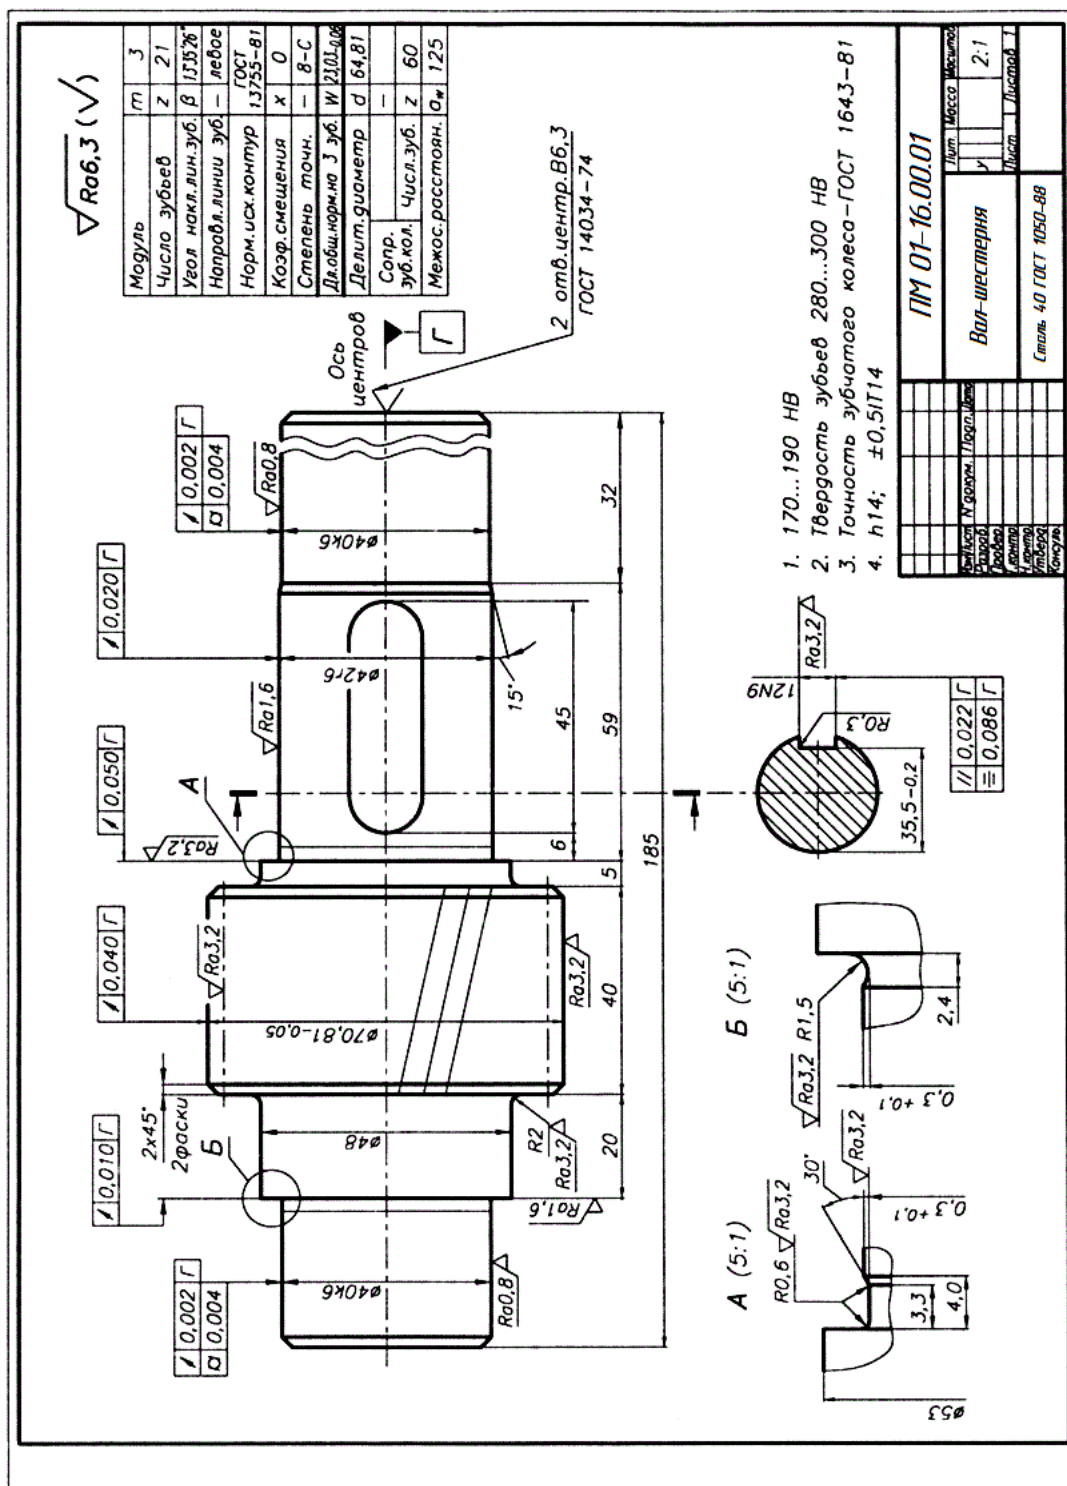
Пример рабочего чертежа цилиндрической вал-шестерни
